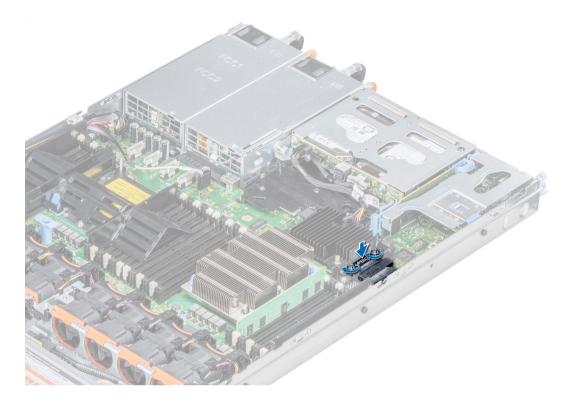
Instalación del cable de la tarjeta controladora de almacenamiento integrada
